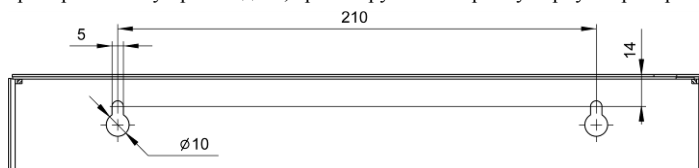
Элементы крепления корпуса прибора ПКП-128
